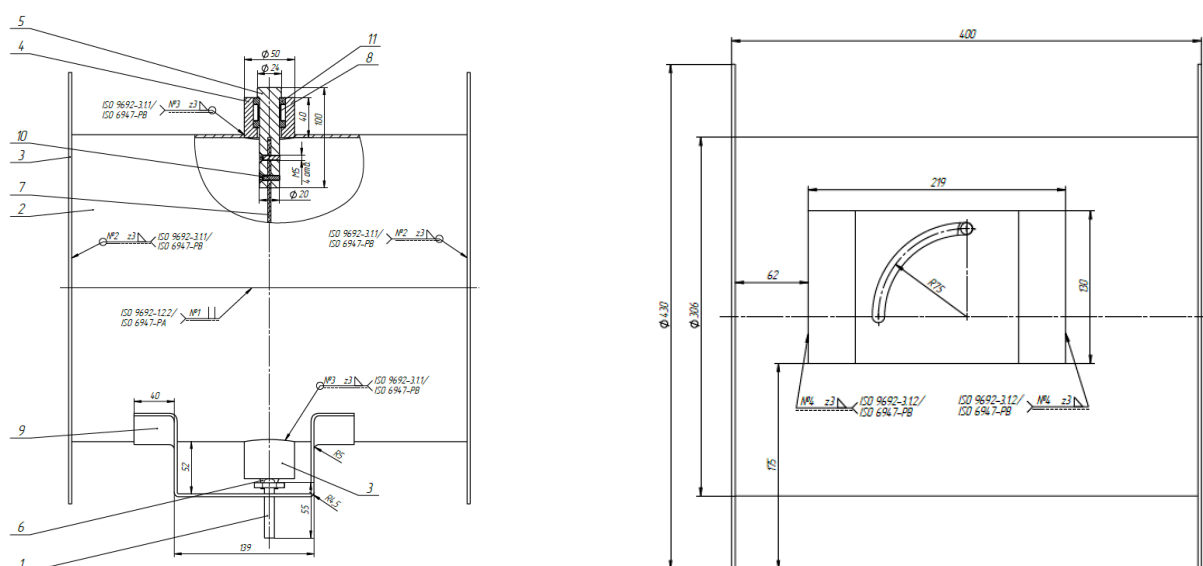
Зварні шви промислової вентиляційної заслінки
